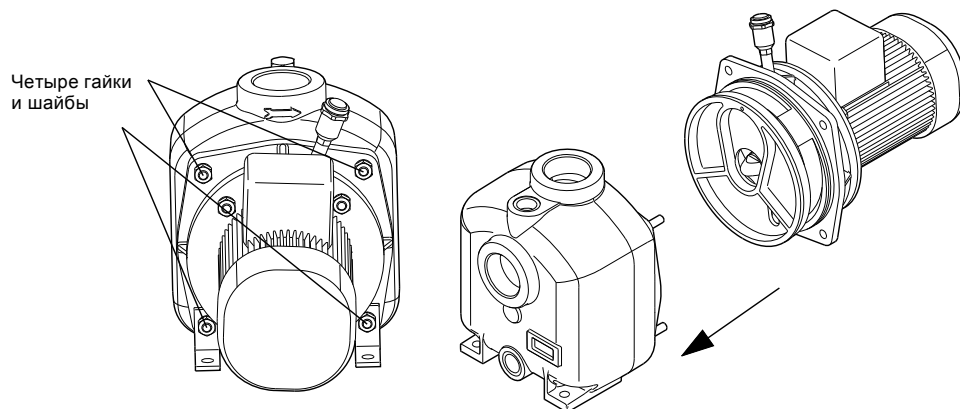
Демонтаж крышки корпуса насоса с двигателем
